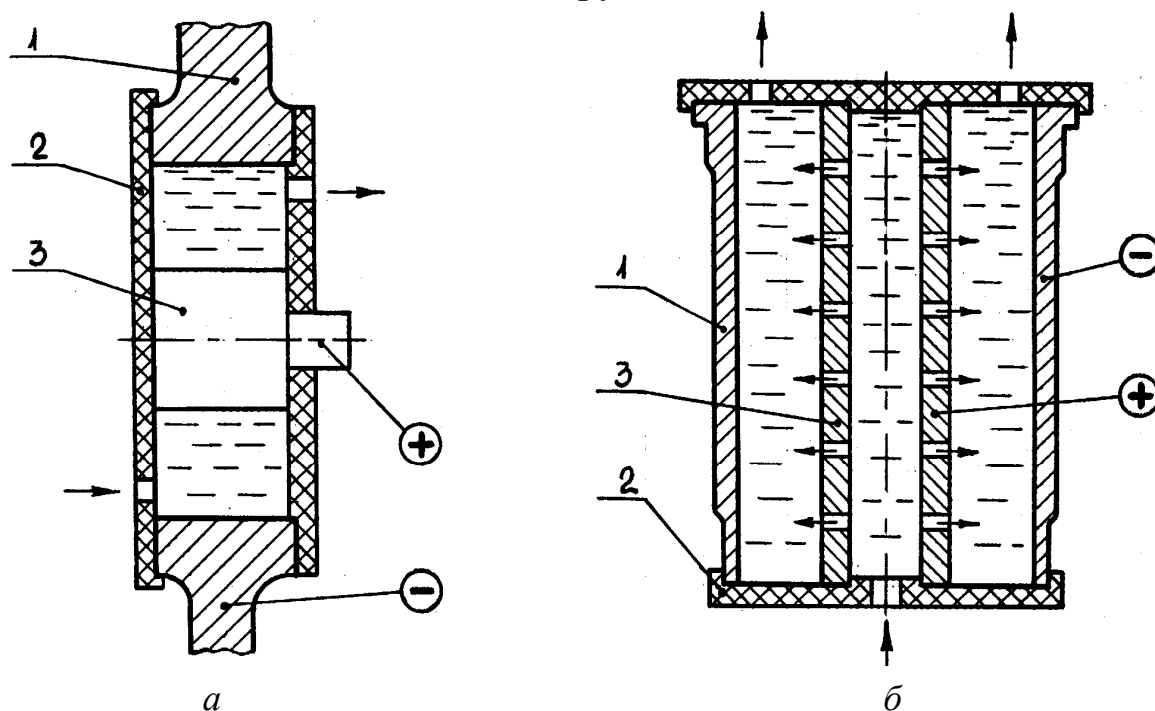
Схемы электроосаждения металла в проточном электролите: а—сплошной проток; б—проток струями; 1—деталь; 2—анод; 3—полукорпус гальванической ячейки; → — направление движения электролита
